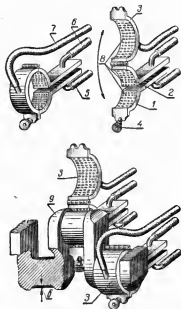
Схема нагрева шеек коленчатого вала при помощи разъемного индуктора:
